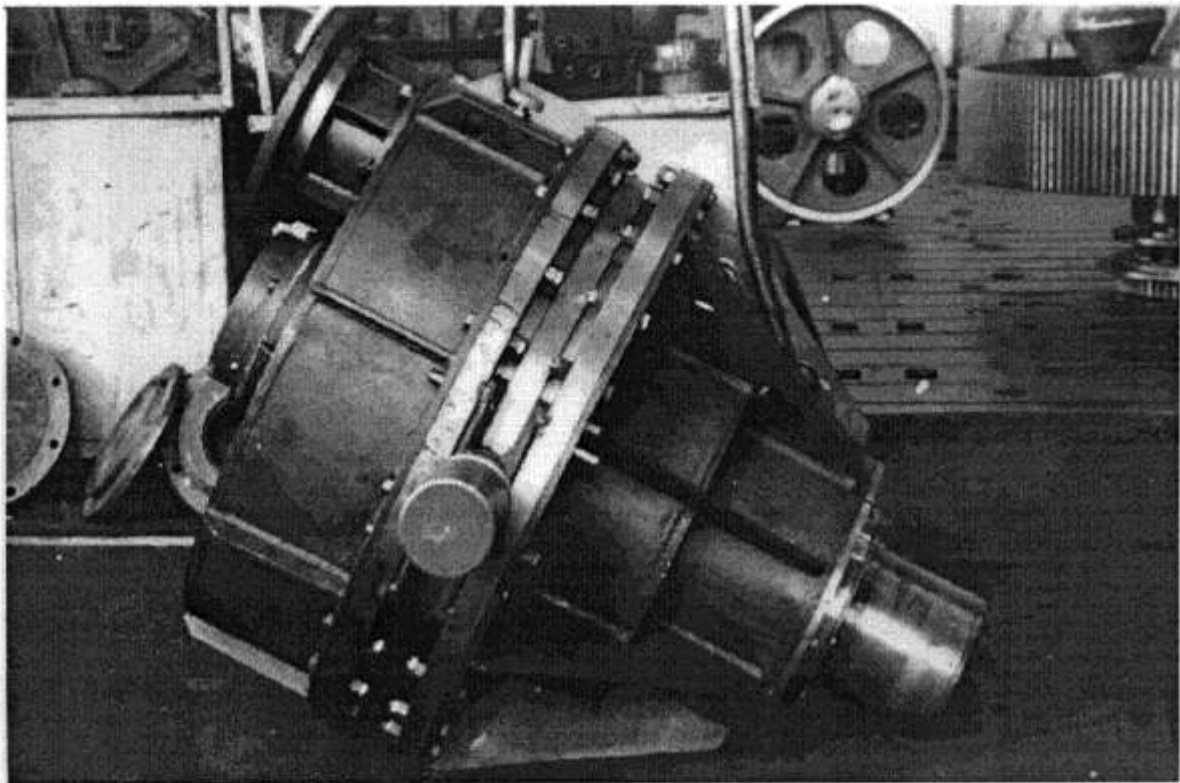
Редуктор с промежуточными телами качения ПК-823 привода классификатора
